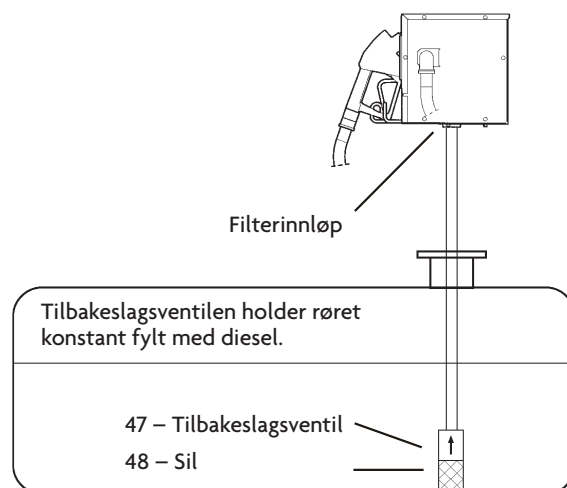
Installering av tilbakeslagsventil og sil
